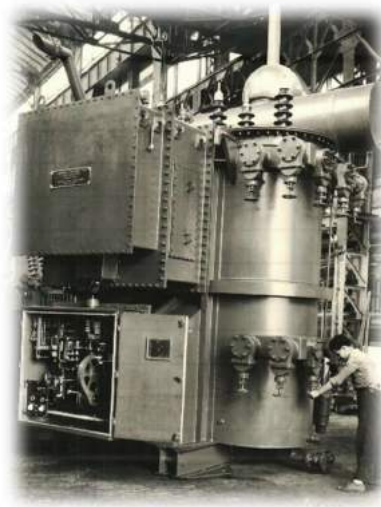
Vista lado conmutador UNR-33 de 17 posiciones.
